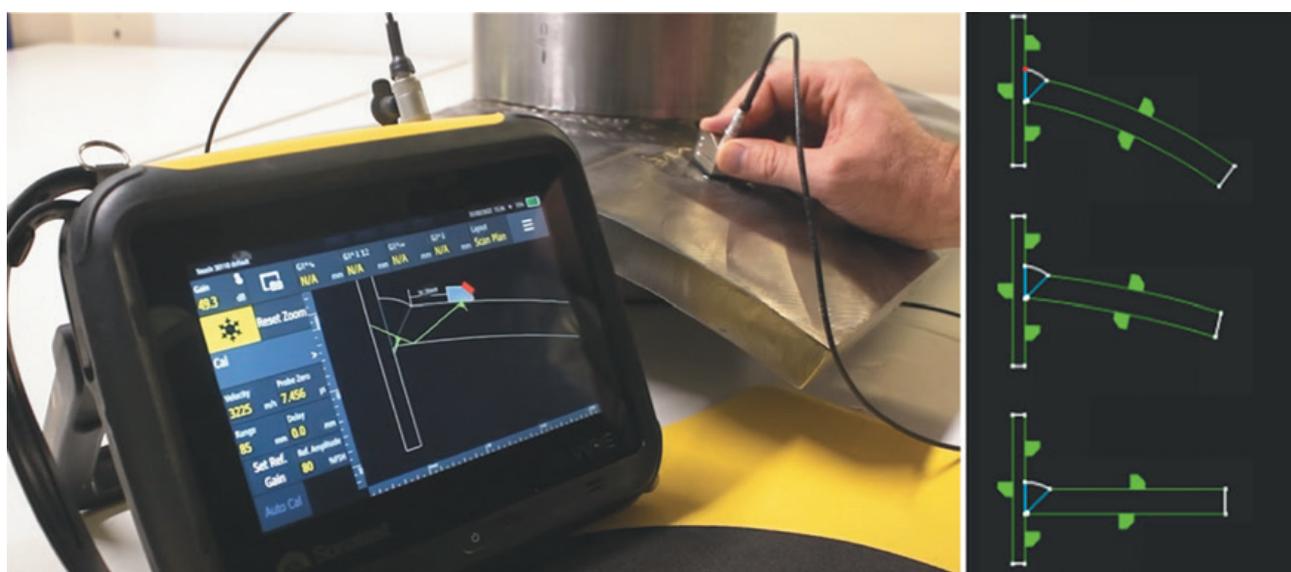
Контроль сварного шва приварки патрубка
